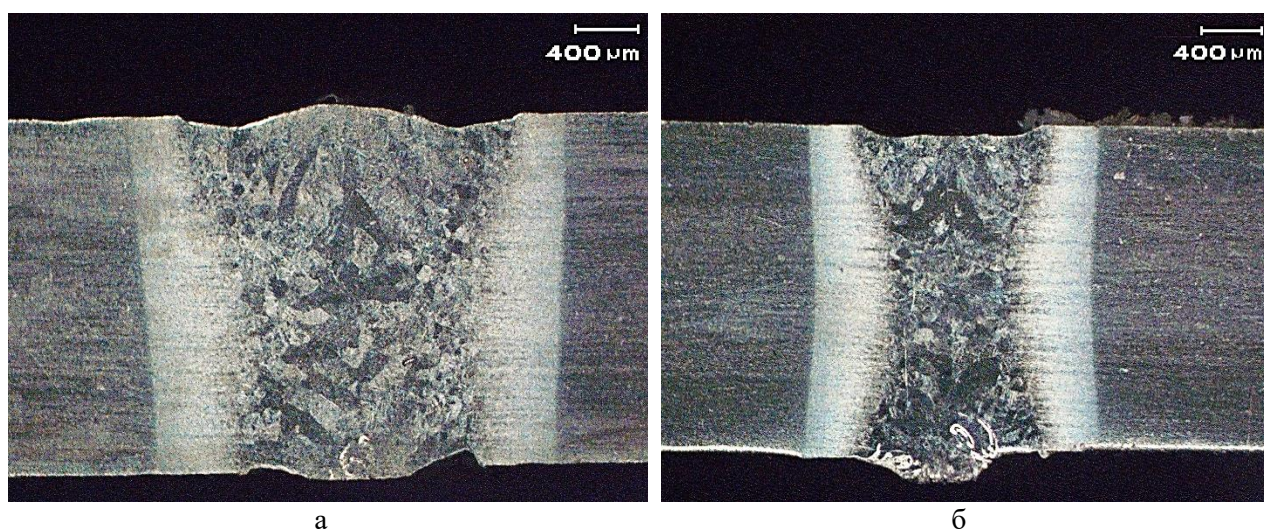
Дефекты сварки: а) подрез корня шва; б) провисание шва.
